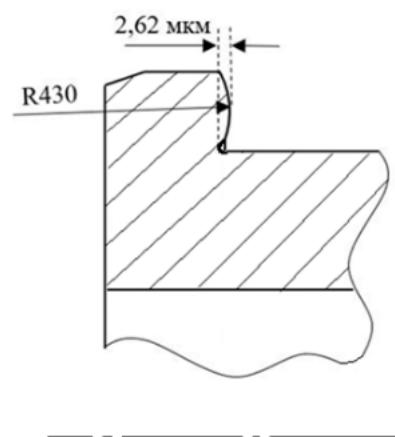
Эскиз фрагмента внутреннего кольца подшипника с выпуклым торцом
